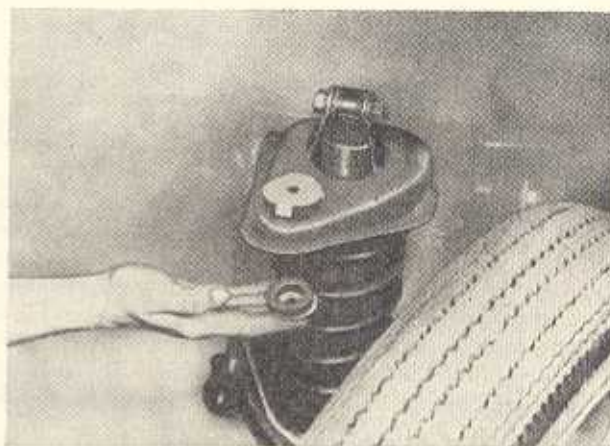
Hintere Karosseriebefestigung, Baumuster 353
